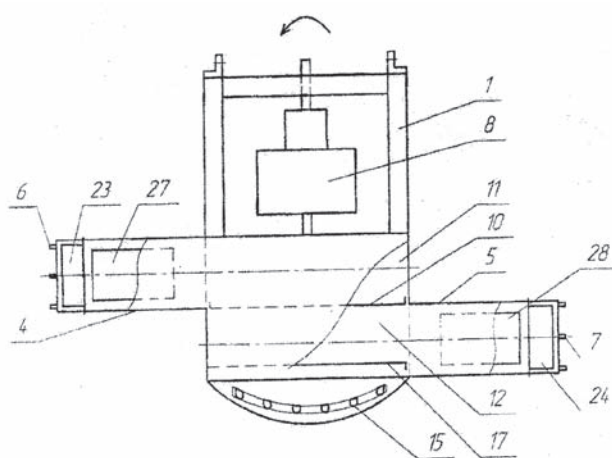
Компоновочная схема опрыскивателя (вид сверху).
